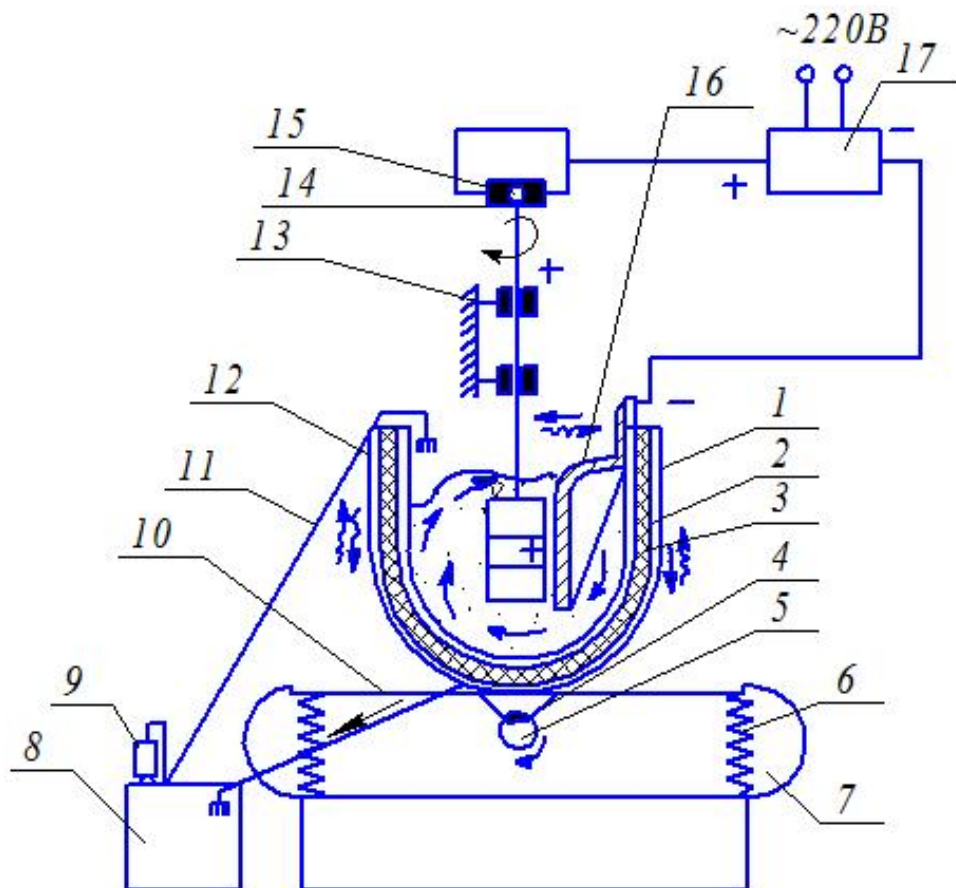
Схема пристрою для віброабразивної електрохімічної обробки:
